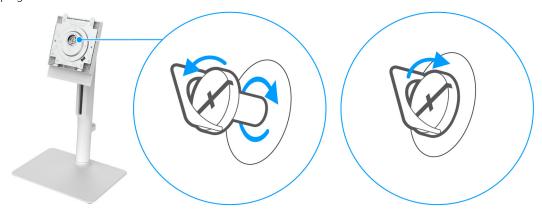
Serrer la vis pour fixer l'ensemble de la charnière
